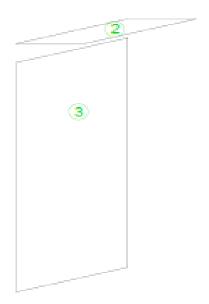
Сборка деталей 2 крыши и левой боковой части 3
